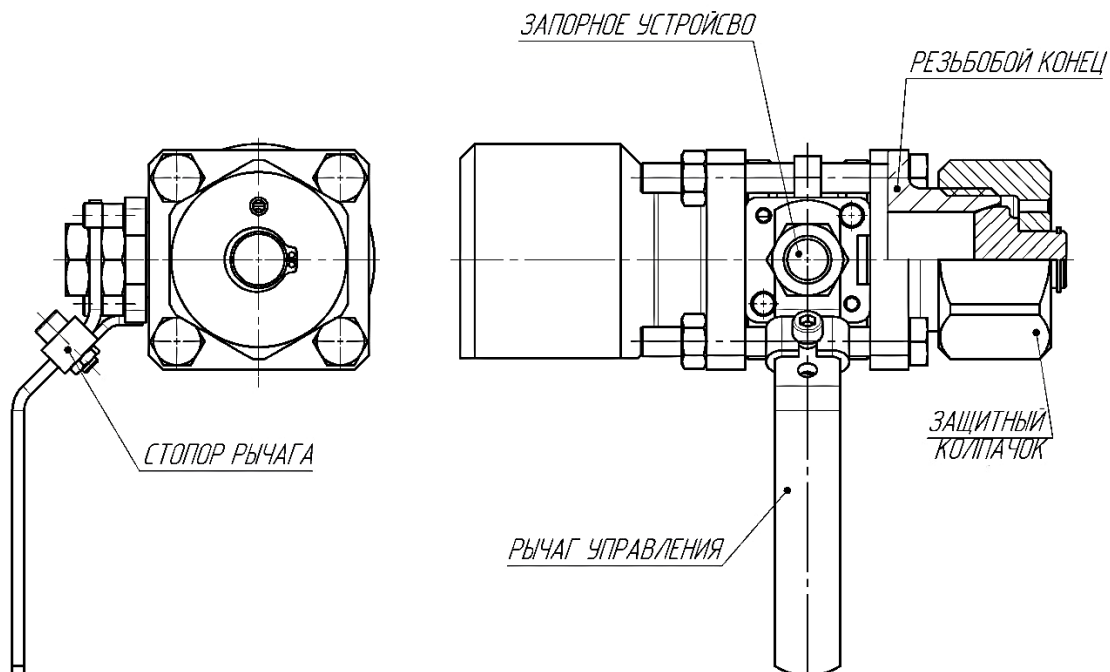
Запорное устройство для дренажа и вентиляции
